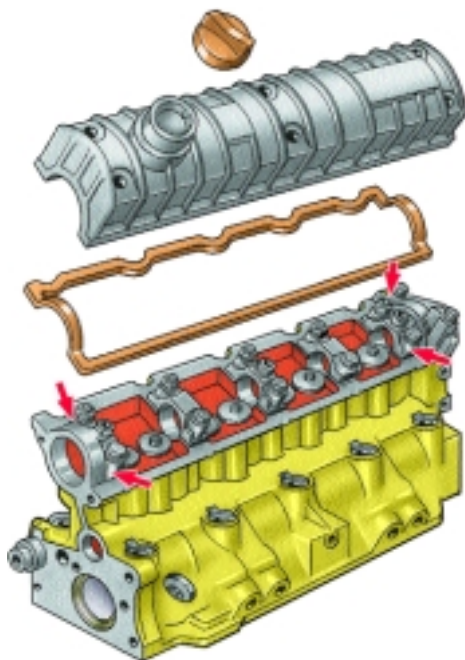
Места нанесения силиконового герметика на головку блока цилиндров двигателя мод. F3R 272
